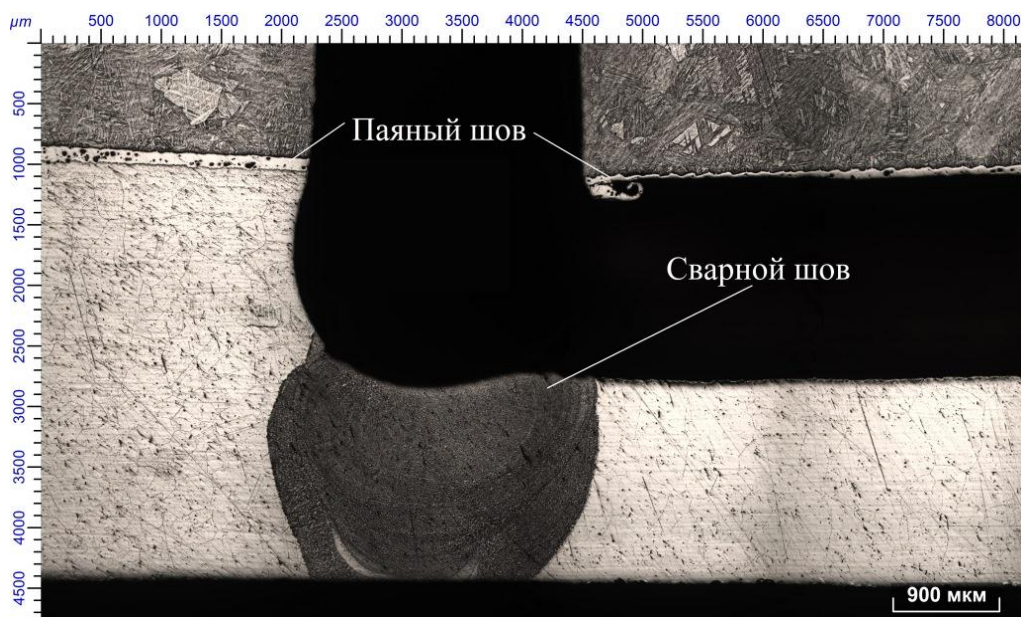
Сварной шов паяных оболочек
